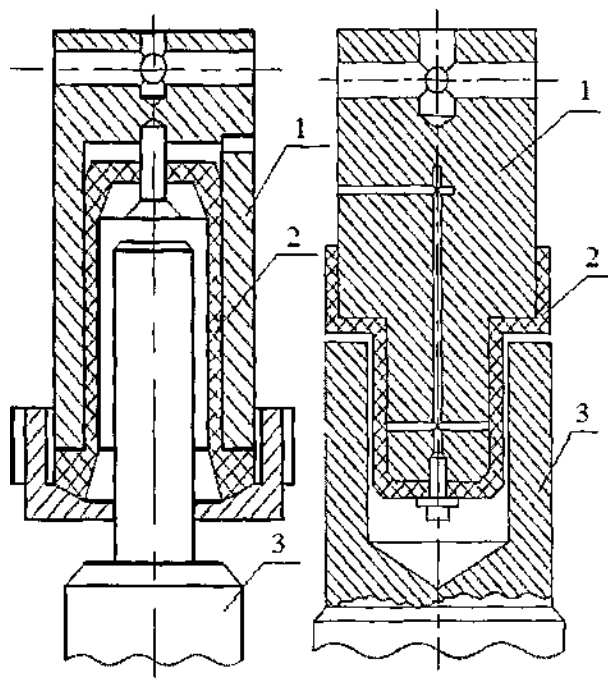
Камерний захоплювальний пристрій із пневматичним приводом.
